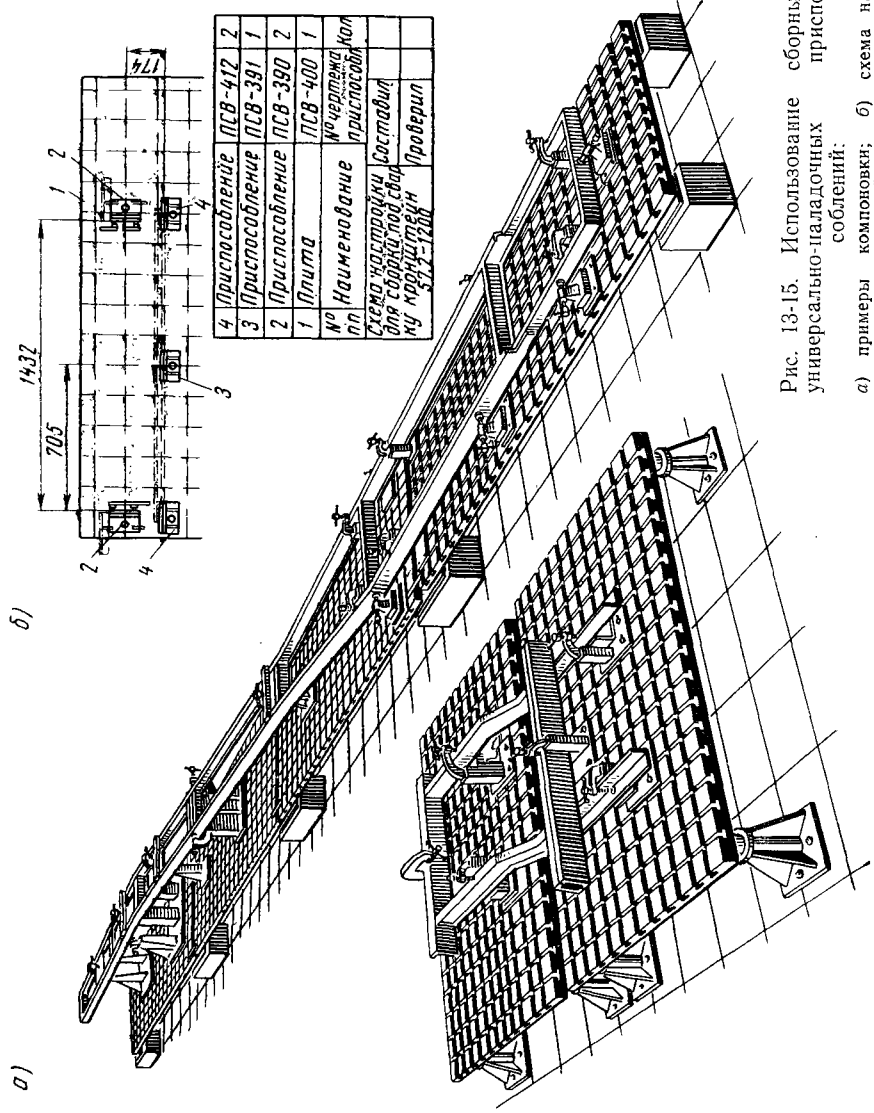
Использование сборных универсально-наладочных приспособлений:
